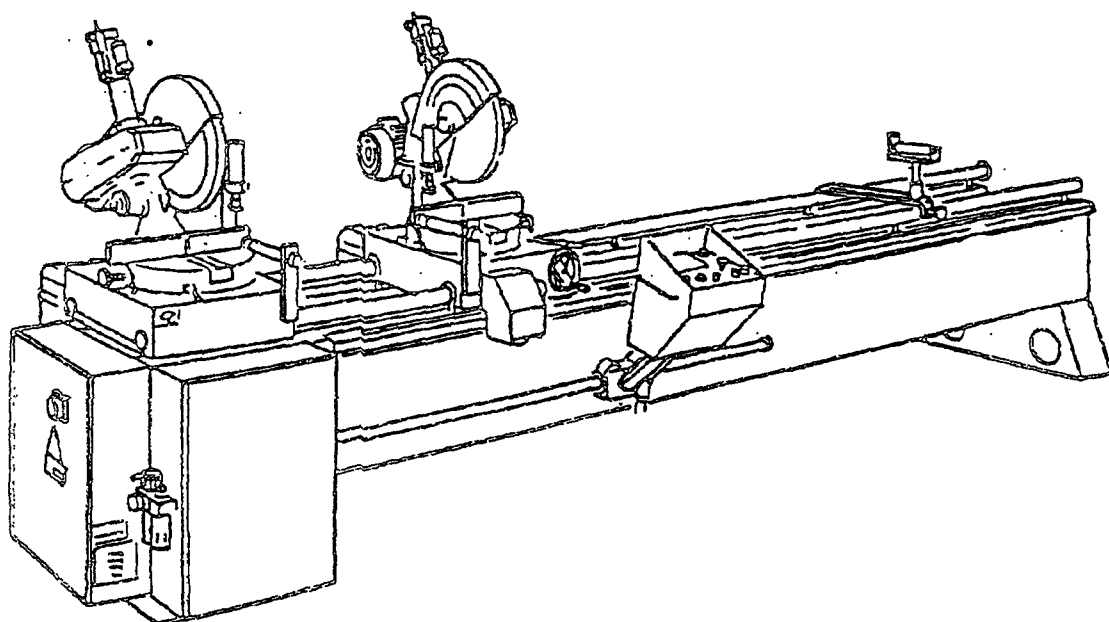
Круглопильний верстат з двома головками. Поворотні різальні головки з подаванням робочого матеріалу зверху. Вид спереду
